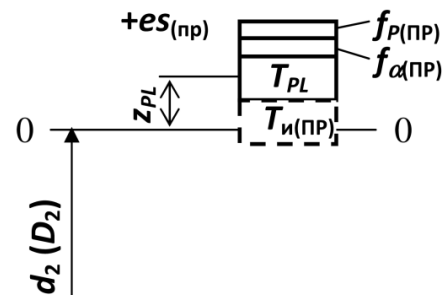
Схема расположения полей допусков проходного резьбового калибра Р-ПП
